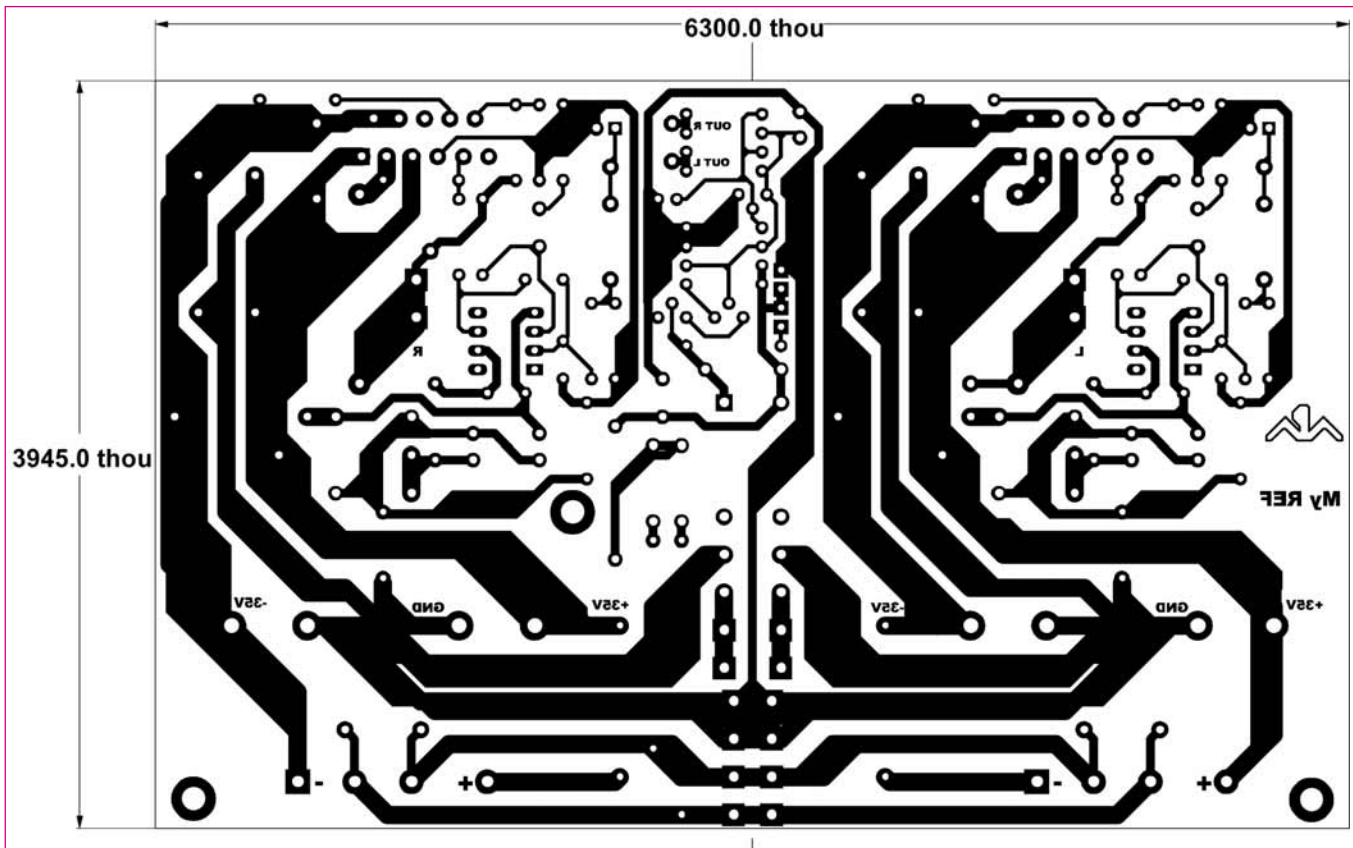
PCB vista lato rame. Dimensioni reali: 100 x 160 mm.
